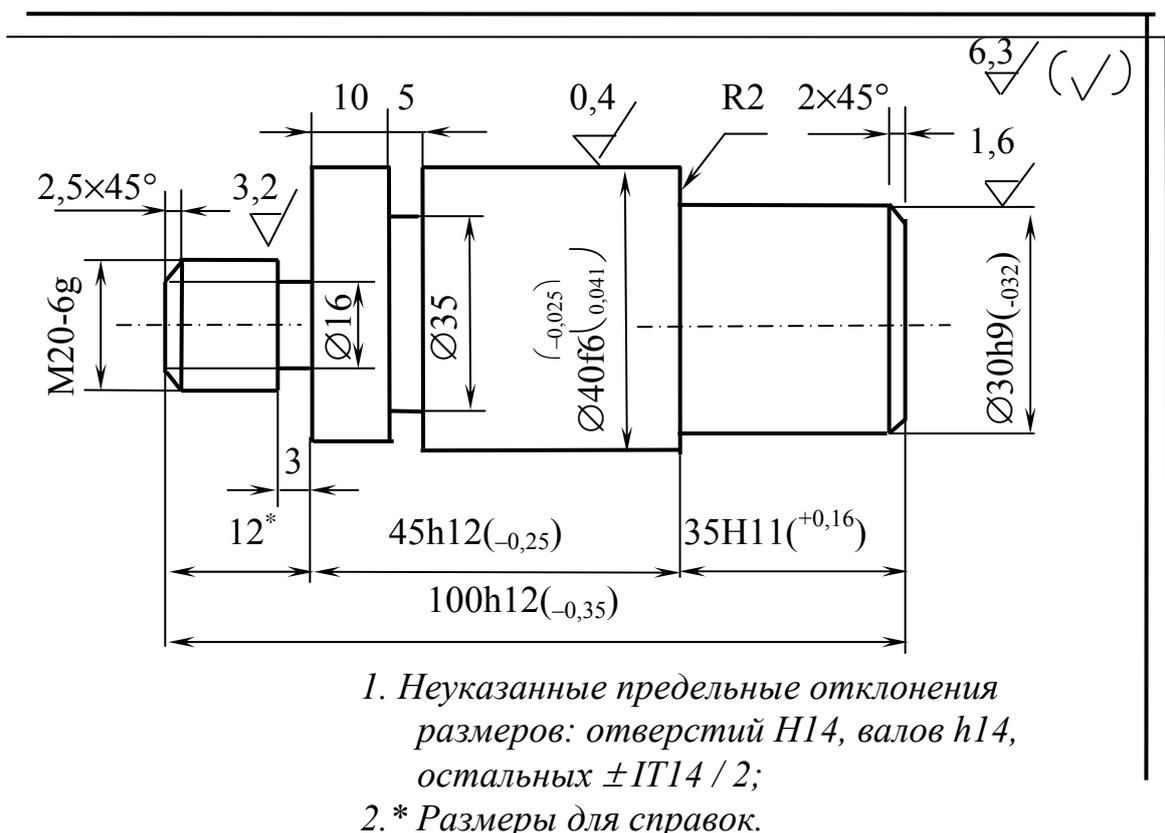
Обозначение размеров, полей допусков (предельных отклонений), справочных размеров и шероховатостей поверхностей
